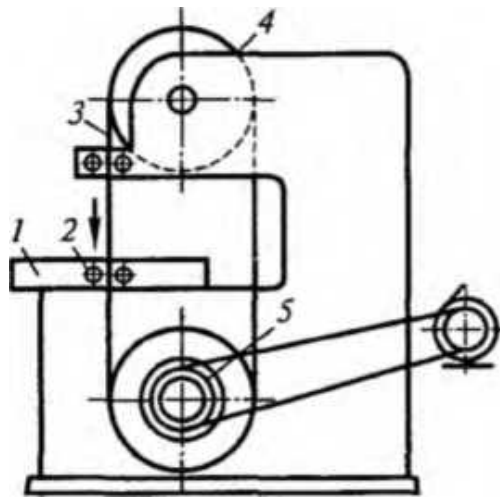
Схема стрічкових пилки: 1 – стіл для установки заготовок; 2 – напрямні ролики; 3 – ножові полотна; 4, 5 – шківни
